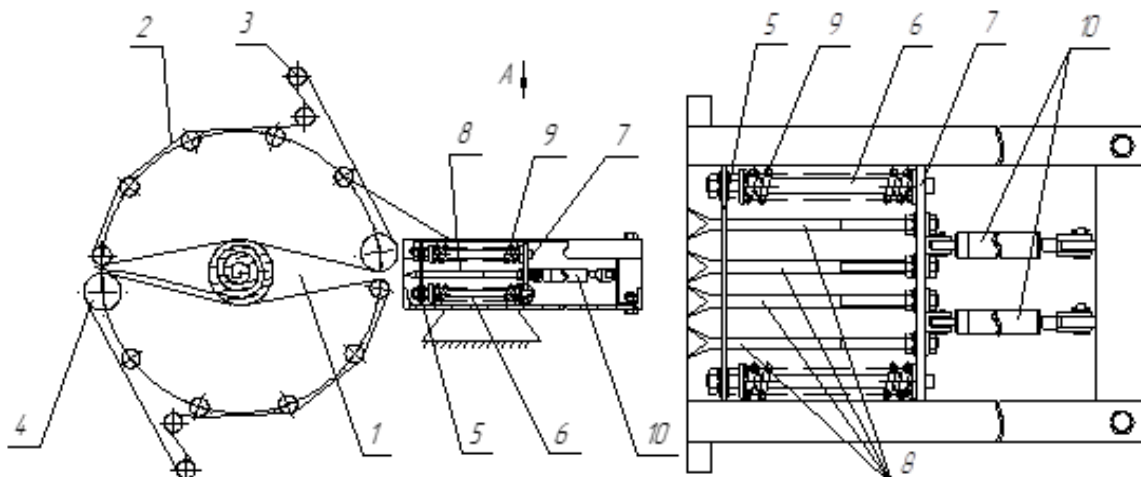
Механізм плющення: 1 – прес-камера; 2 – ремінний робочий елемент; 3 – натяжний механізм; 4 – провідний барабан; 5 – напрямна плита; 6 – направляючі пальці; 7 – рухома плита; 8 – пуансони; 9 – відвідні пружини; 10 – гідроциліндри.
